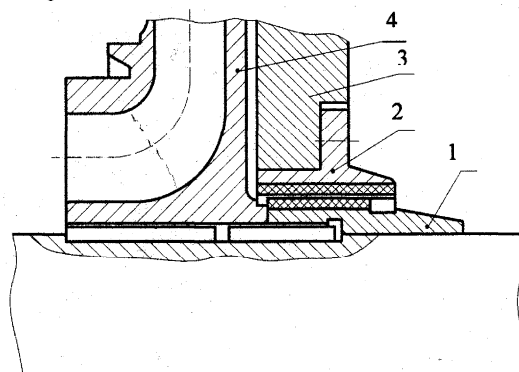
Промежуточная радиальная опора центробежного насоса. 1 – ступица рабочего колеса, наплавленный материал ТМ-1; 2 – втулка радиальной опоры, наплавленный материал ТМ-1; 3 – направляющий аппарат; 4 – рабочее колесо.
